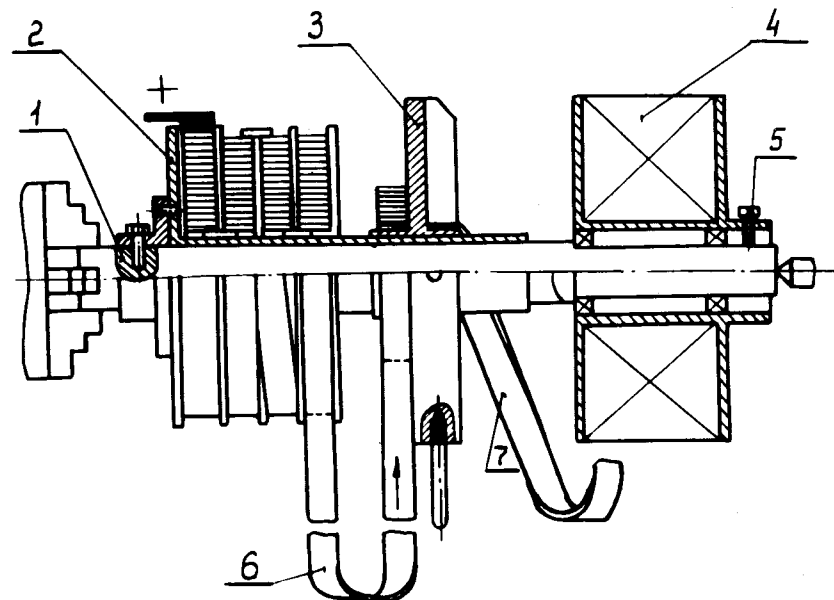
Приспособление для намотки наружной секции соленоида. 1 - ведущий вал; 2 - каркас соленоида; 3 - планшайба; 4 - питающая катушка; 5 - стопорный винт; 6, 7 - ленточный сверхпроводник.
